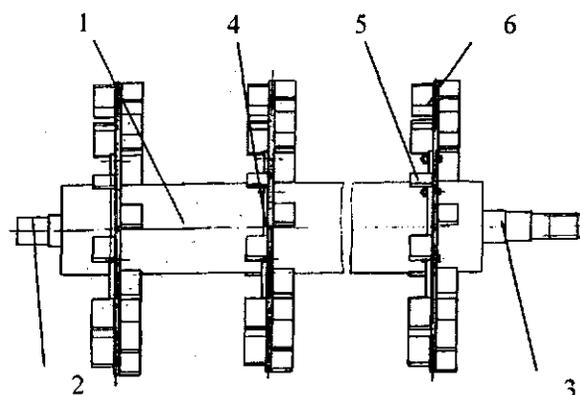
Конструктивная схема фрезбарабана: 1-труба; 2,3-фланцы; 4-несущие диски; 5-крепёжные болты; 6-сменные режущие элементы
